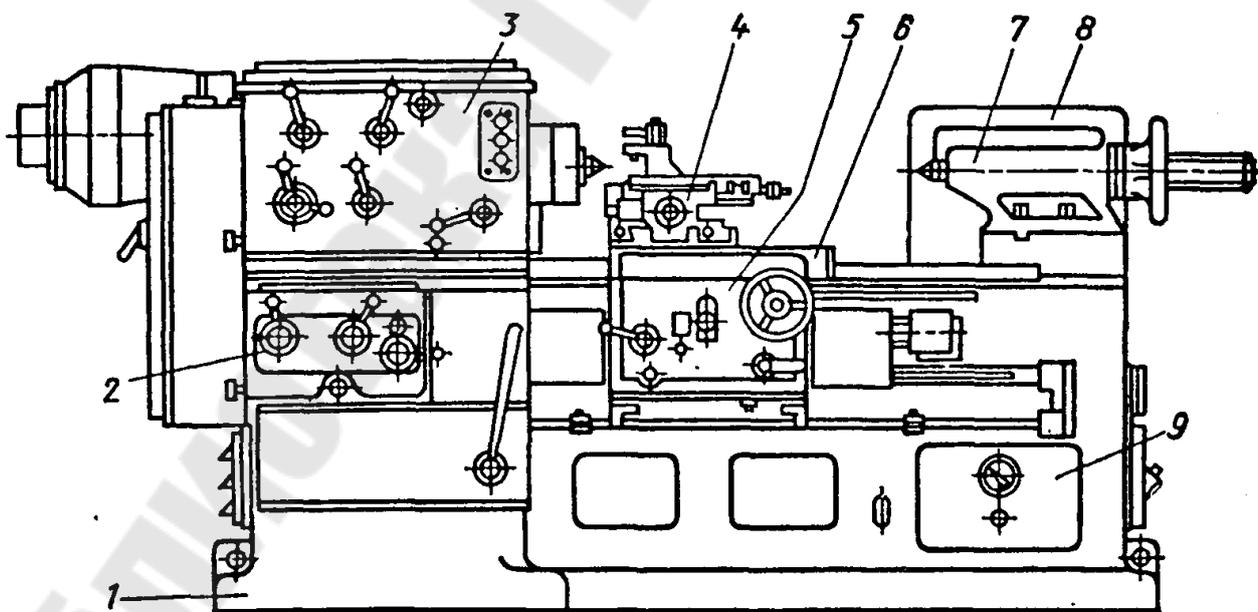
Общий вид токарно-затыловочного станка
